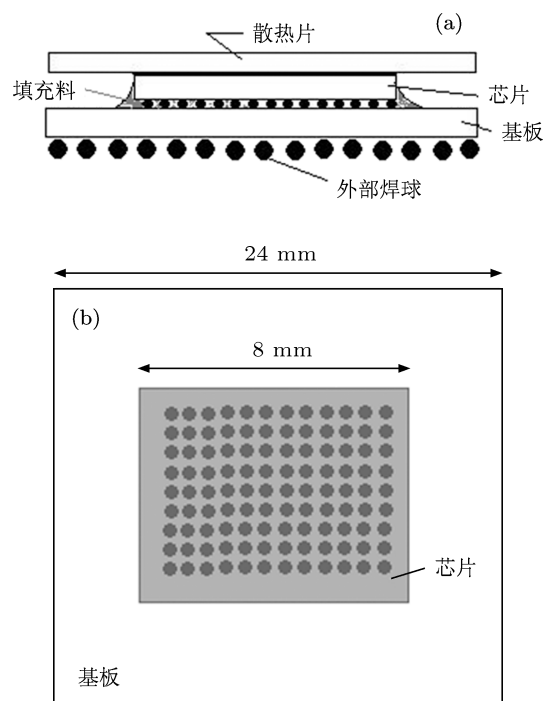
FC-PBGA 封装器件的结构示意图 (a) 侧视图; (b) 顶视图
